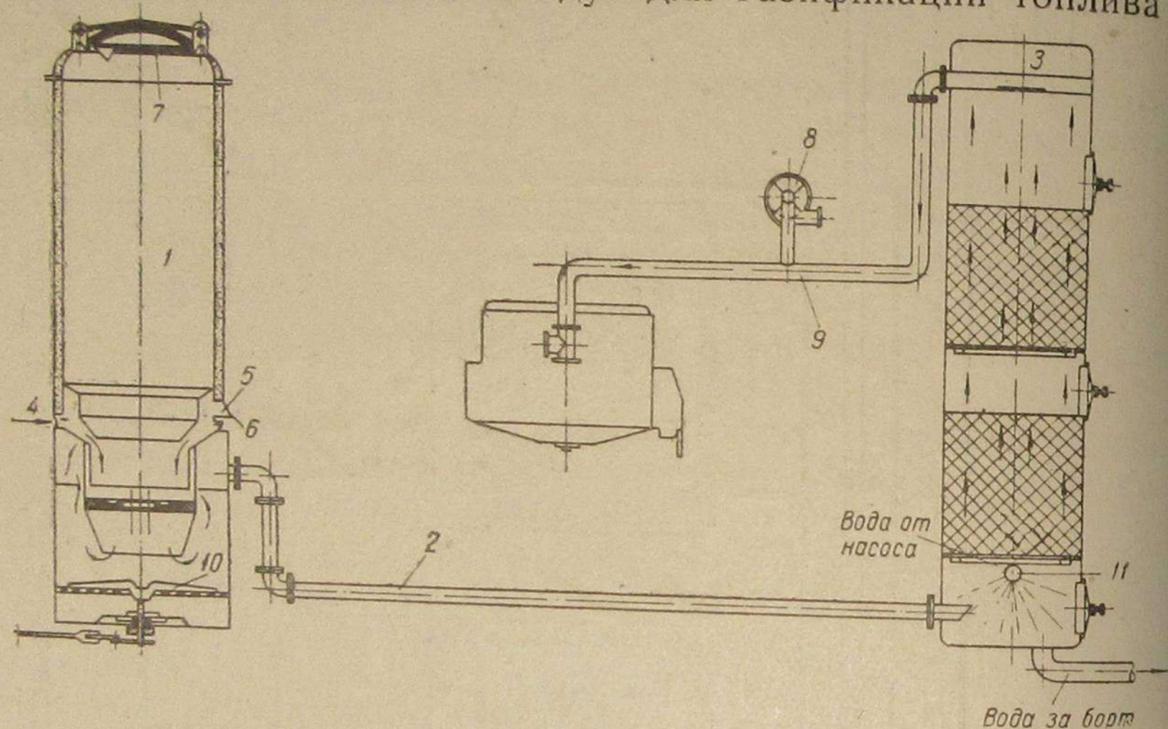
Схема газогенераторной установки для двигателя 6ГСЧ $\frac{9,5}{11}$
